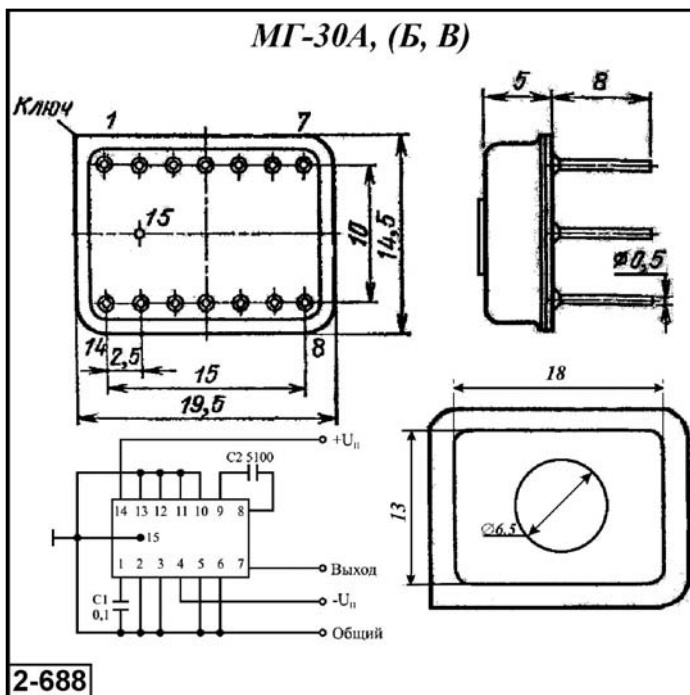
Внешний вид и габаритные размеры ТПУ: МГ-30, МГ-32 и МГ-33
